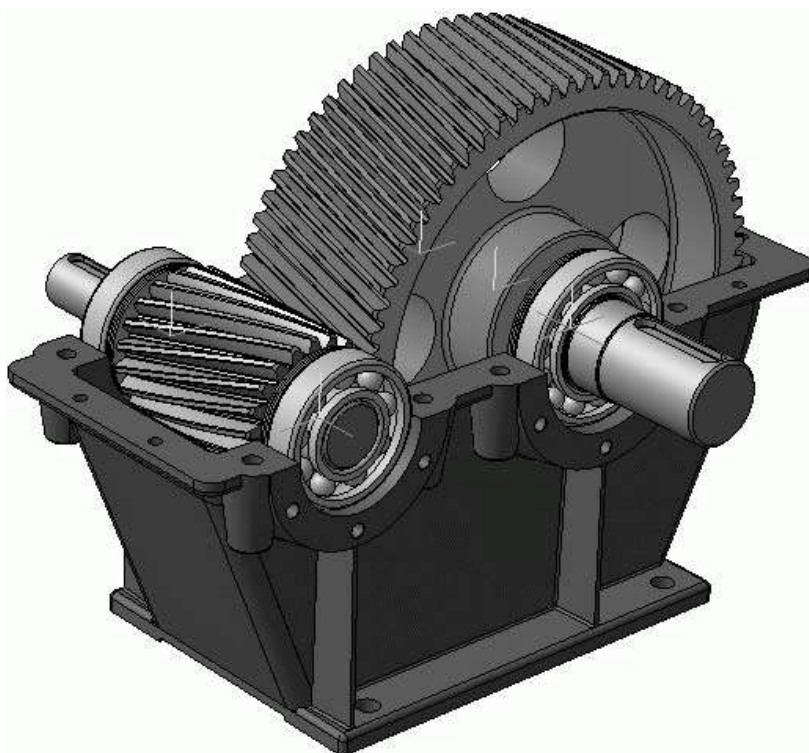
Сборка подшипниковых узлов и вставка зубчатой передачи в корпус
